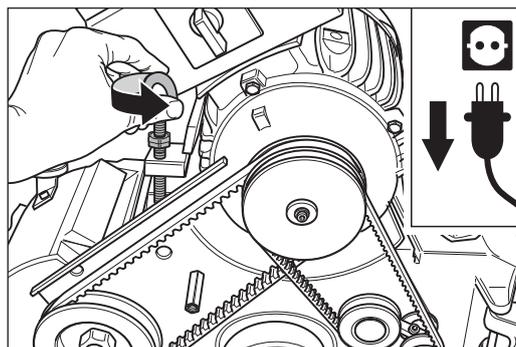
Die Ringschraube am Motor gegen den Uhrzeigersinn drehen.
